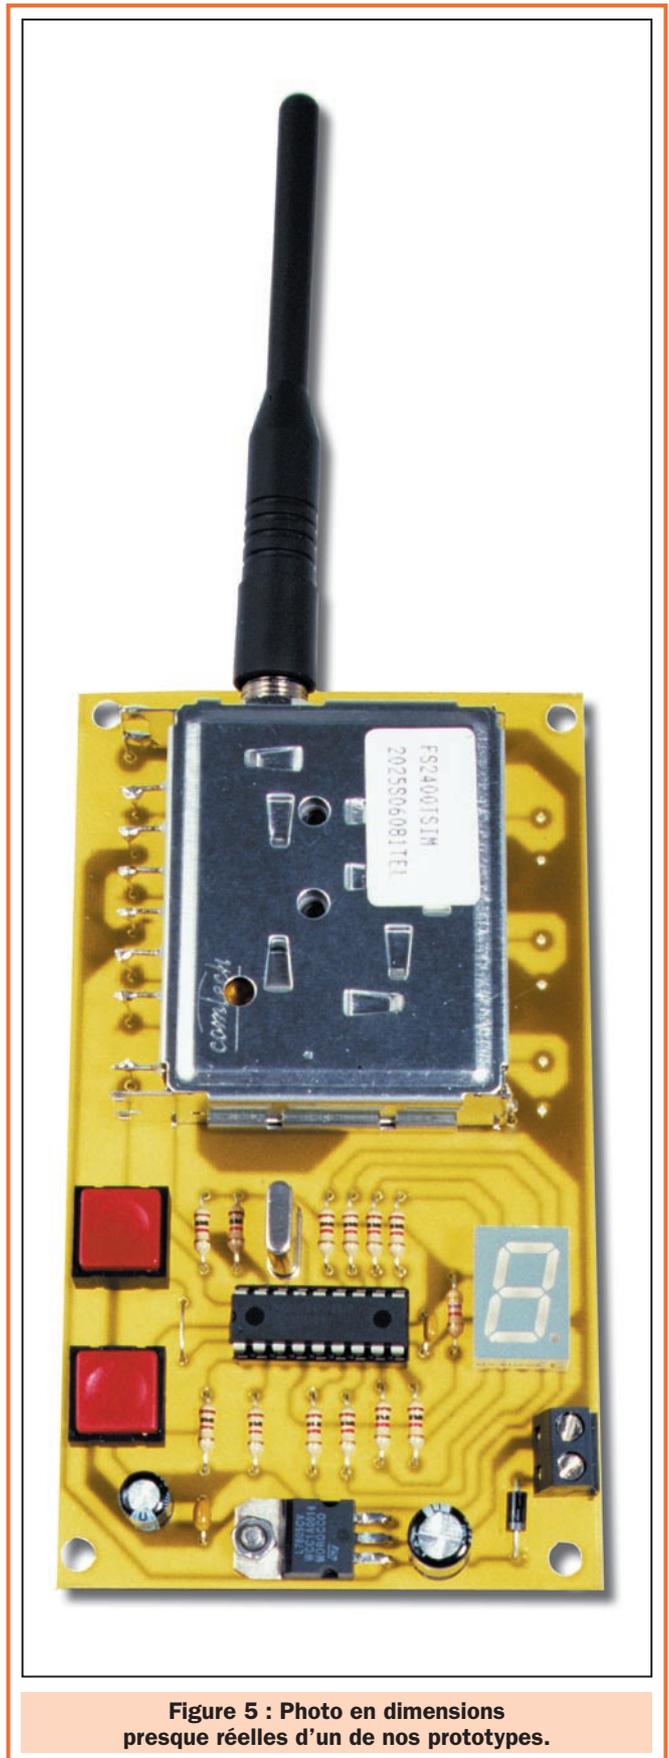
Photo en dimensions presque réelles d'un de nos prototypes.
